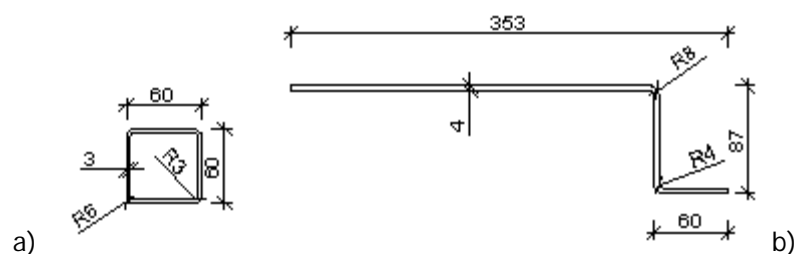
Secção transversal do perfil FH. a)20'HC; b)40'HC.
